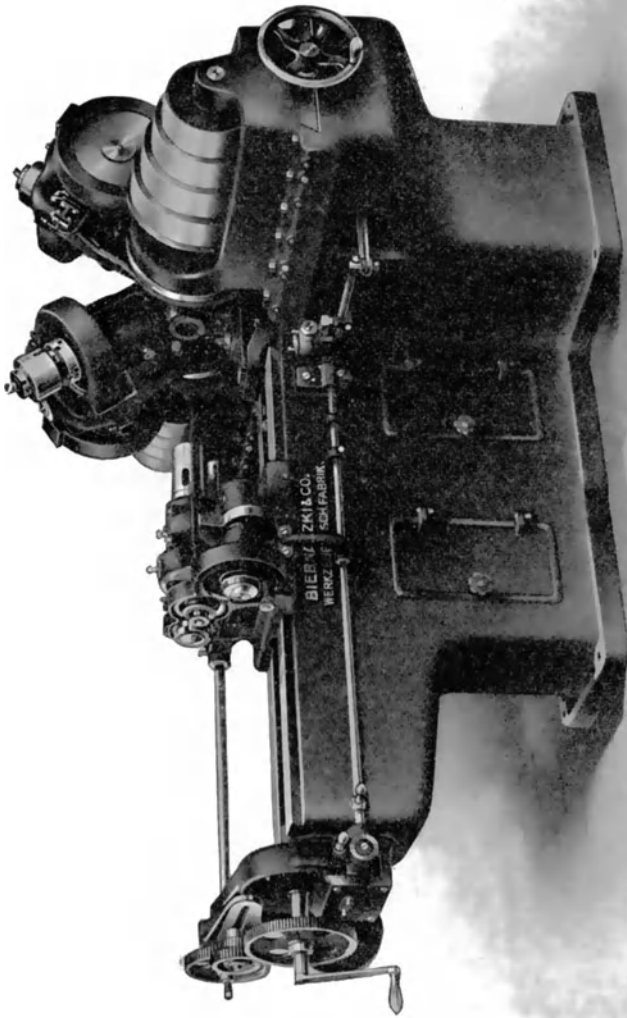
Spiralbohrerfräsmaschine von Biernatzki & Co.
